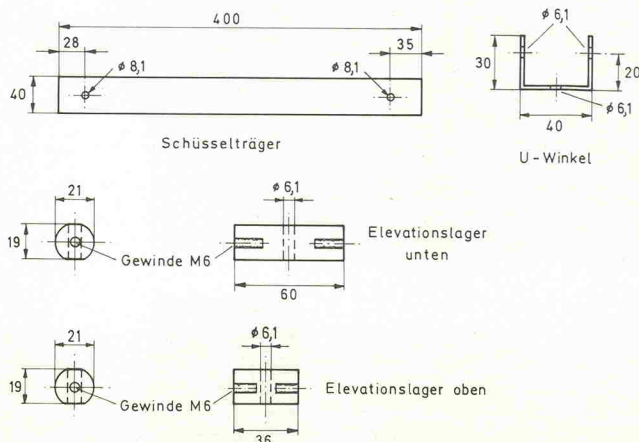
Schlüsselträger und Elevationslager sind wieder recht einfach herzustellen.
